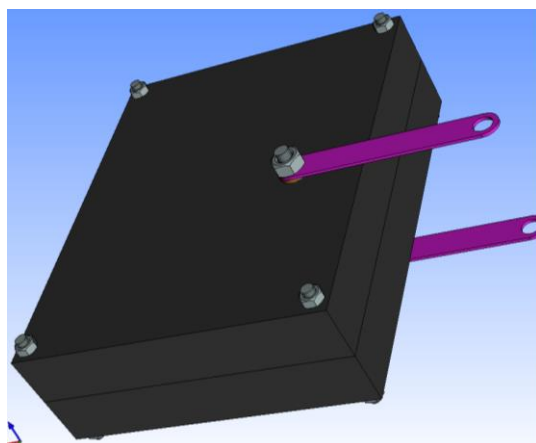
Внешний вид корпуса двухуровневого датчика с выходными рычагами
